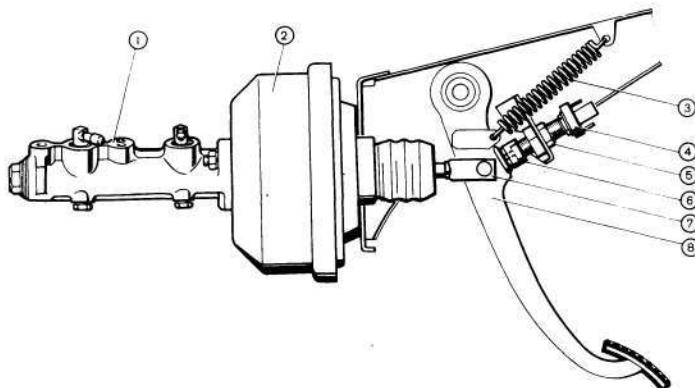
Привод тормозов: 1 — главный цилиндр гидросистемы тормозов; 2 — вакуумный усилитель; 3 — оттяжная пружина педали; 4 — выключатель стоп-сигнала; 5 — гайка упорного винта; 6 — буфер выключателя стоп-сигнала; 7 — толкатель; 8 — педаль тормоза
